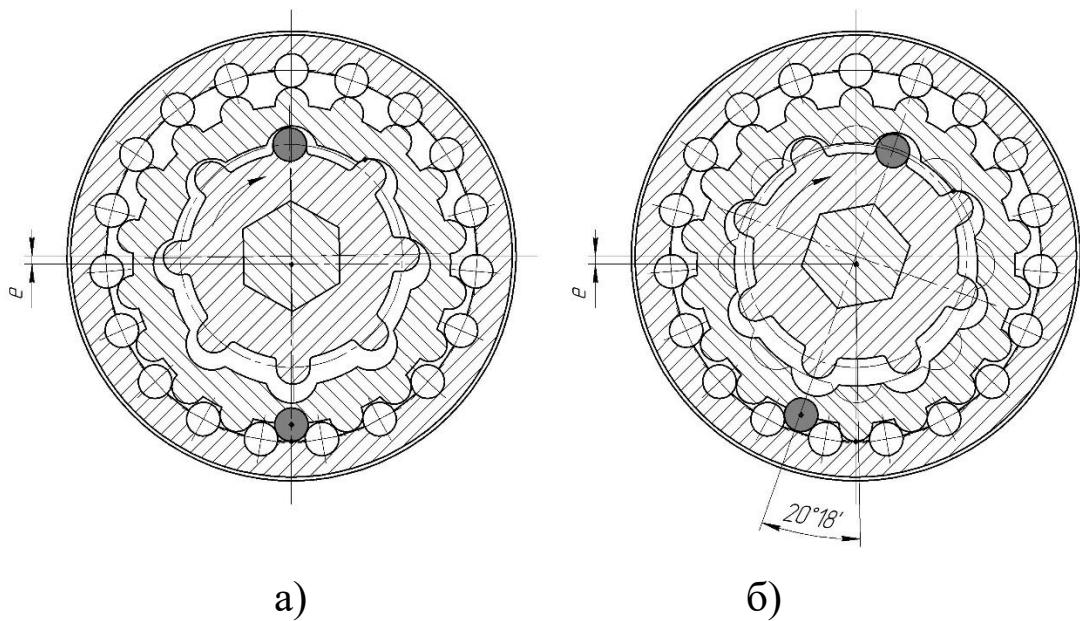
Поперечний переріз планетарно-роторного привода обертання:
